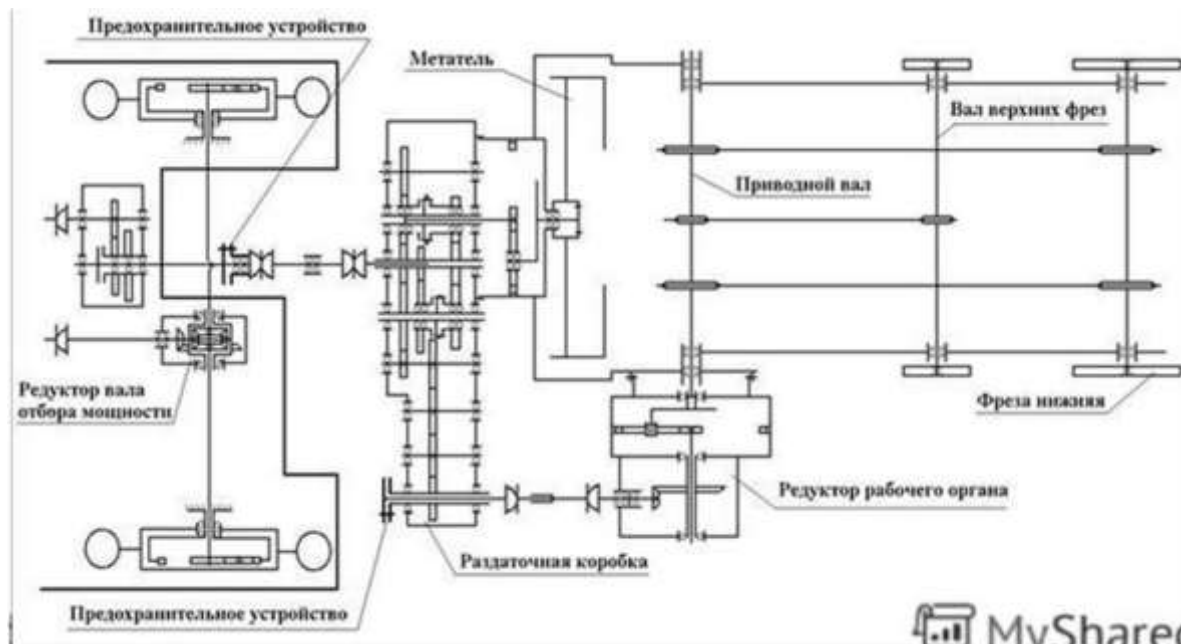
Кінематична схема робочого обладнання ПЗМ-2
